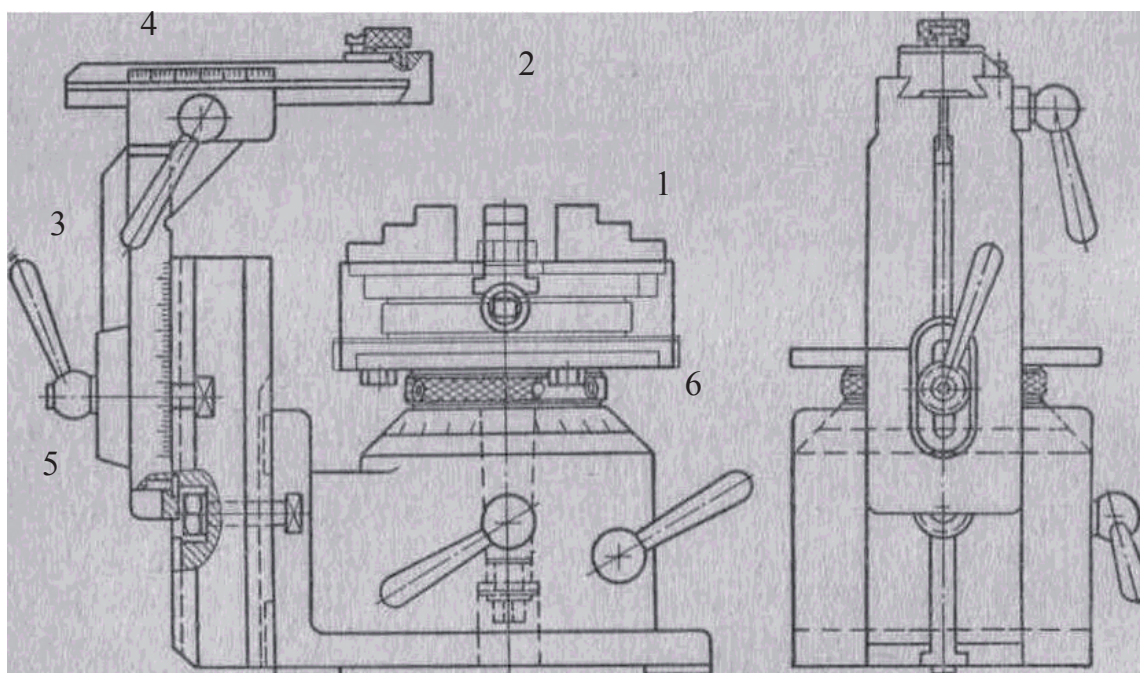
Перенастраиваемое поворотное приспособление для сверления центральных и плановых отверстий в деталях типа диска
